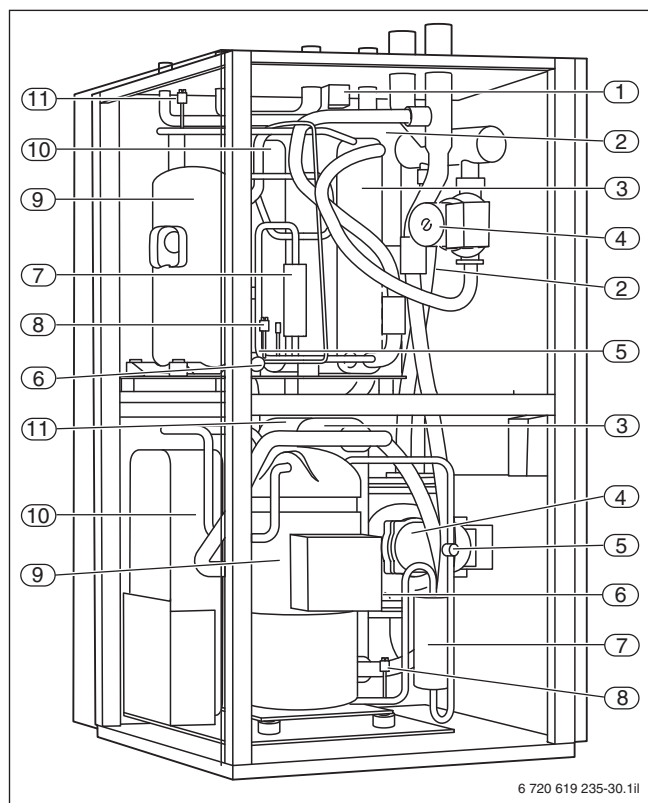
Ausgewählte Bauteile und Baugruppen der Wärmepumpen T 430-1 ... T 600-1
